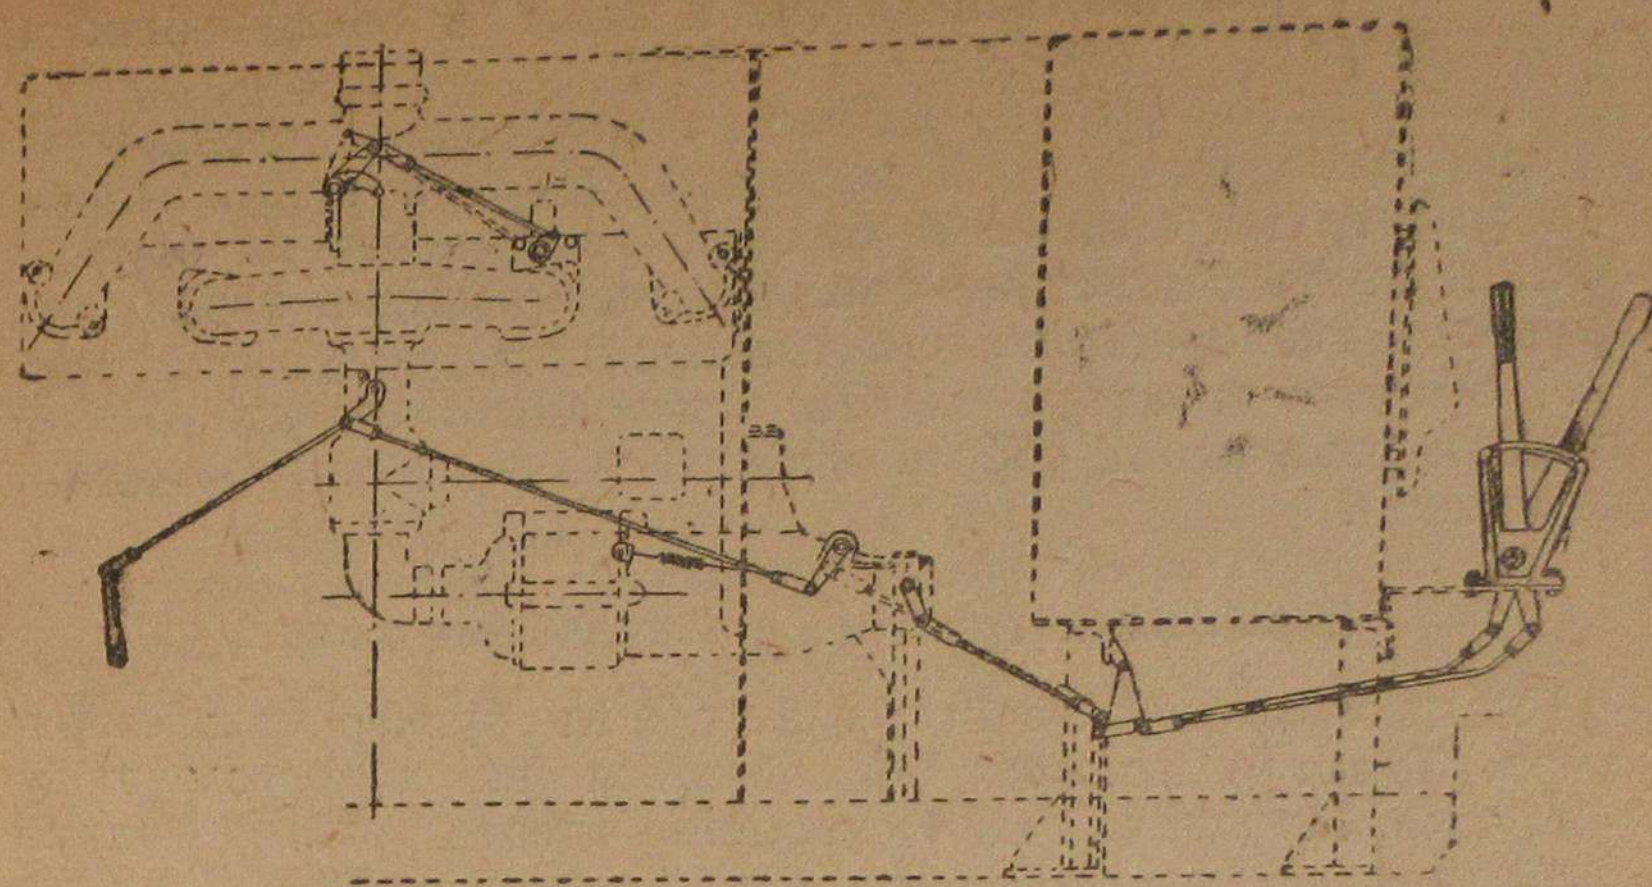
Тяги и рычаги управления газовым двигателем — вид сбоку
